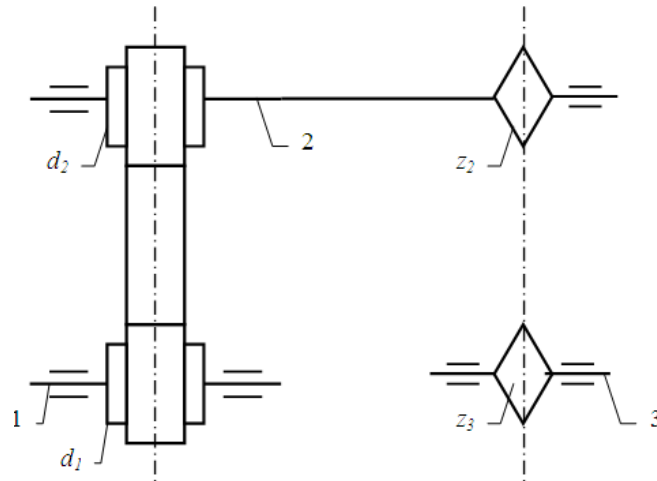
Кинематическая схема привода с ременно-цепным передаточным механизмом
